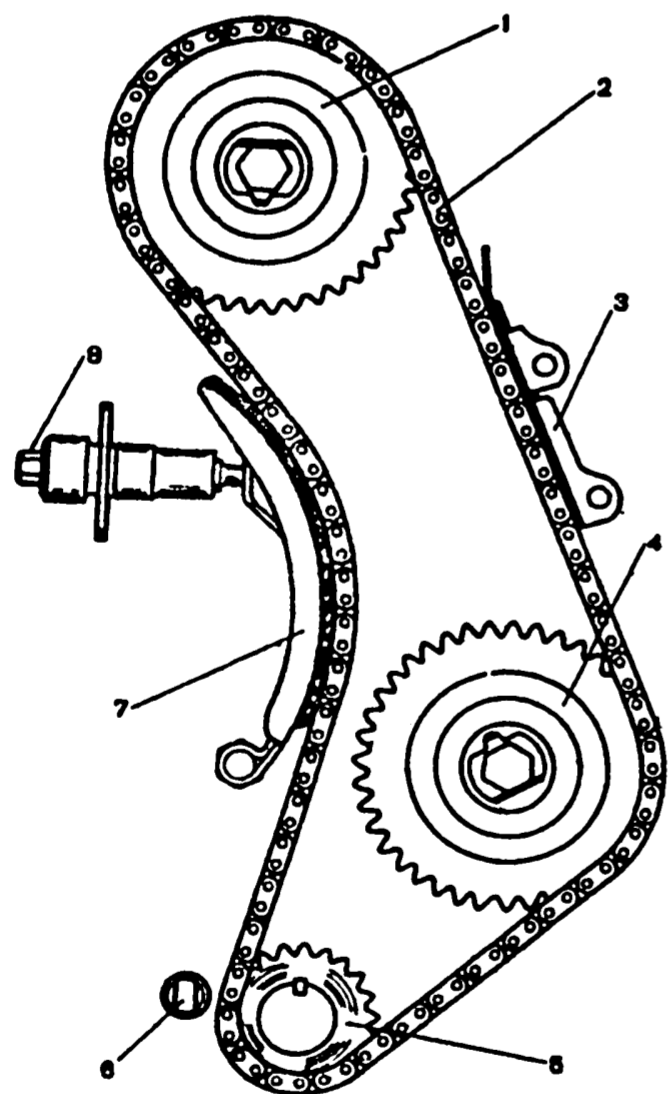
Схема механизма привода распределительного вала: 1 - звездочка распределительного вала; 2 - цепь; 3 - успокоитель цепи; 4 - звездочка валика привода масляного насоса; 5 - звездочка коленчатого вала; 6 - ограничительный палец; 7 - башмак натяжителя; 8 - натяжитель цепи
